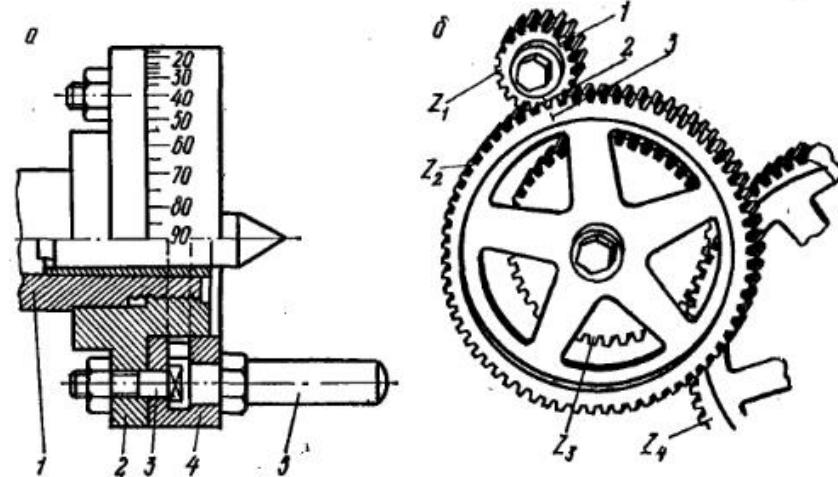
Деление хода многозаходных резьб на заходы поворотом заготовки:
